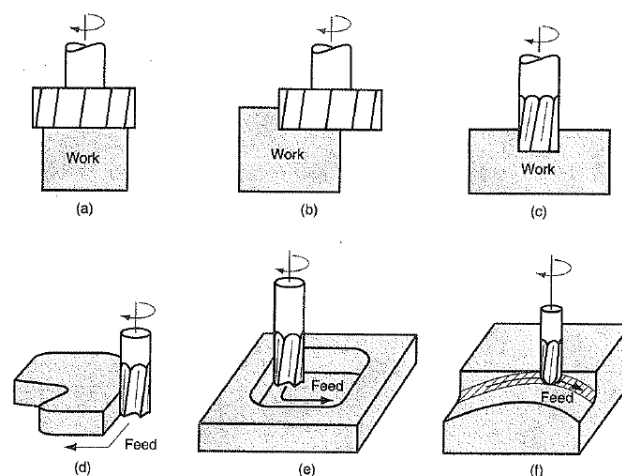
Fresagem de topo: a) facejamento, b) facejamento parcial, c) fresagem frontal de canal, d) fresagem lateral de contorno*, e) fresagem de caixa, e f) fresagem de superfície 3D [2].
